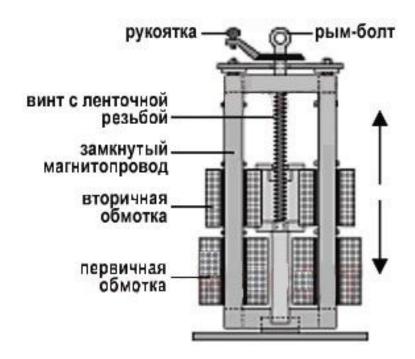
Схема регулирования тока в сварочном трансформаторе с подвижными обмотками
